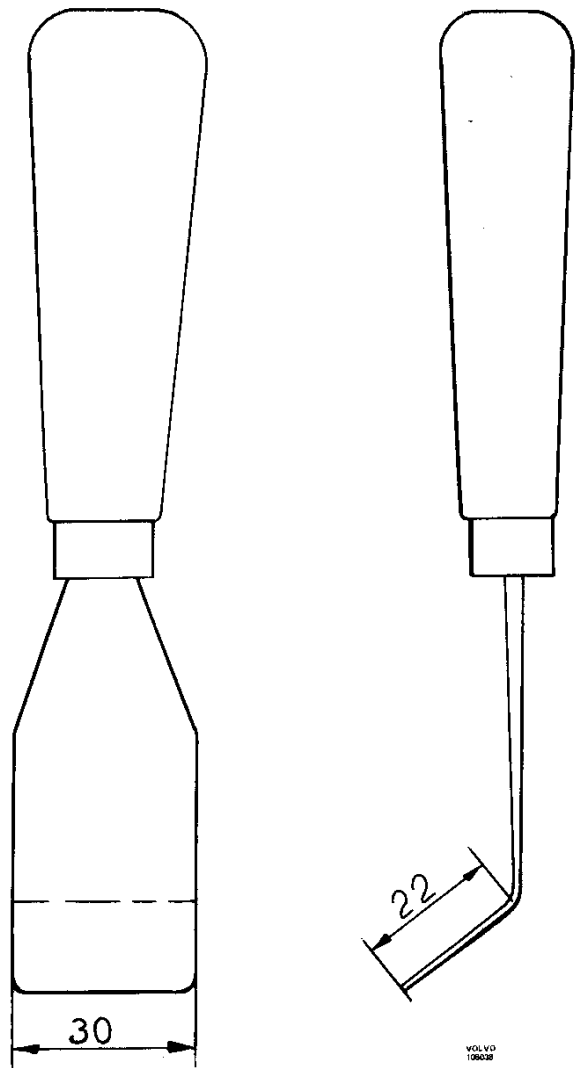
Anfertigung eines Werkzeugs zum Ausbau der Zierleiste für die Frontscheibe
